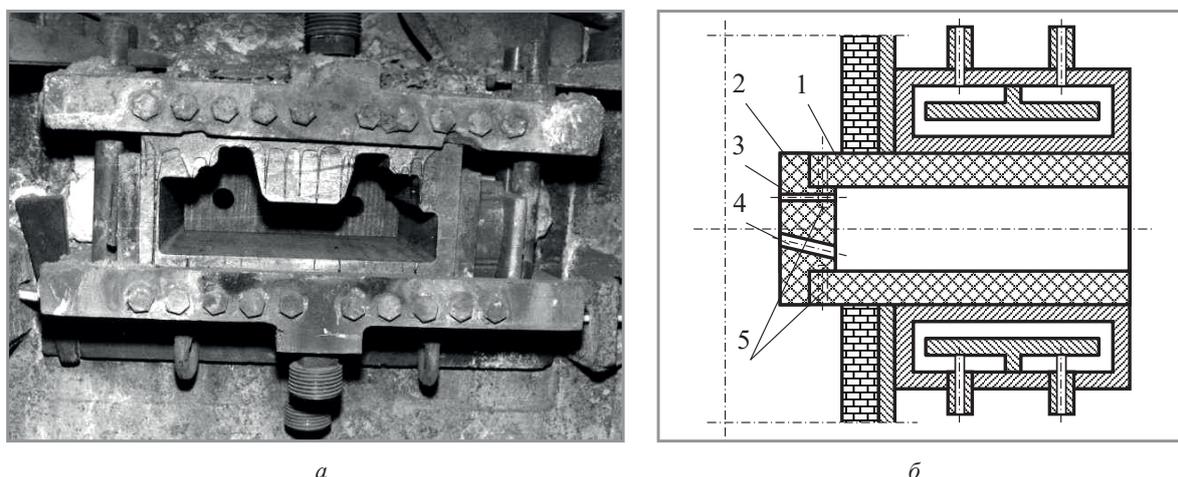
Кристаллизатор (а) и схема установки разделительного устройства (б):
